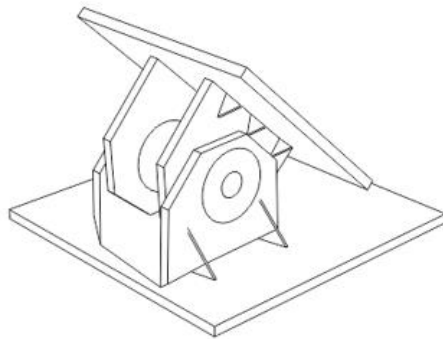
Platina base en acero galvanizado. Propia. Cerón Silvia. 2016.
